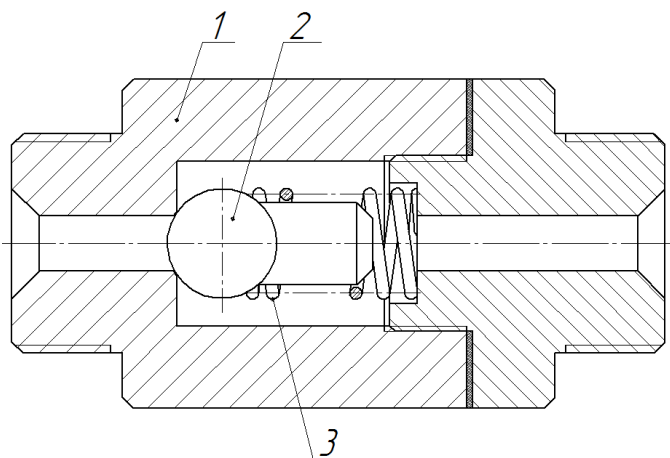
Перепускной клапан: 1- корпус; 2- двойной запорный элемент; 3- пружина клапана
